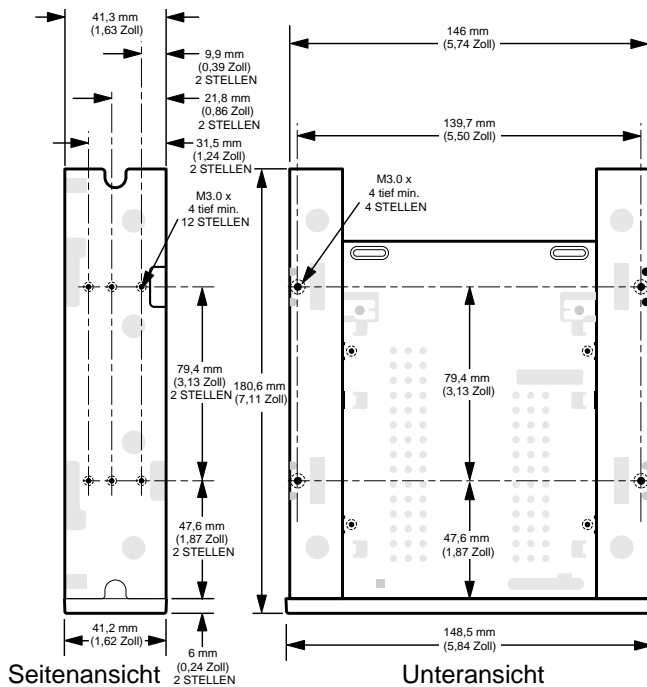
Schraubenbohrungen für interne DAT24-Laufwerke in einer 5,25-Zoll-Konfiguration (mit Einbauhalterungen)
